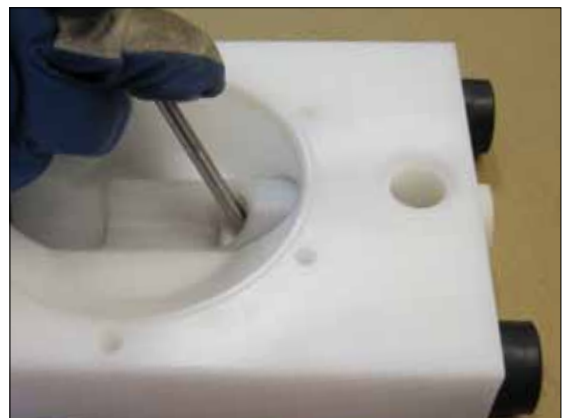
Um das Distanzstück (19) zu entfernen, nehmen Sie ein Stück Kunststoff und schlagen vorsichtig mit einem Hammer um es zu drehen.
